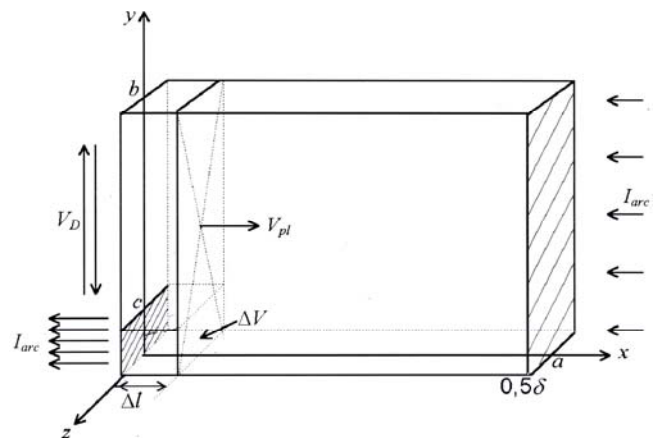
Нагрев пластинчатого электрода током сварки
